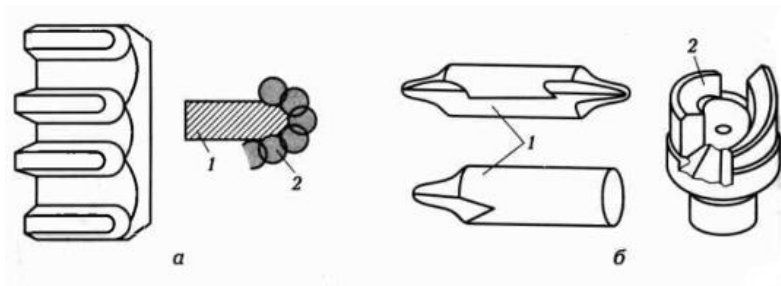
Схема закруглення (а) і конструкції фрез для закруглення зубів (б)
